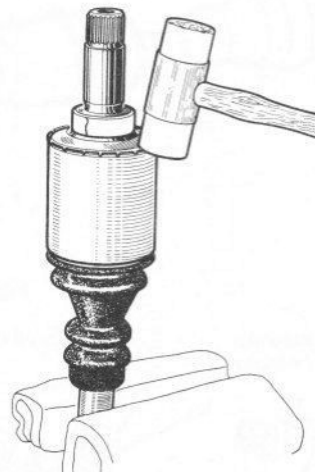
Dégagement du capot en tôle du joint d'arbre de roue (Sec 5)
